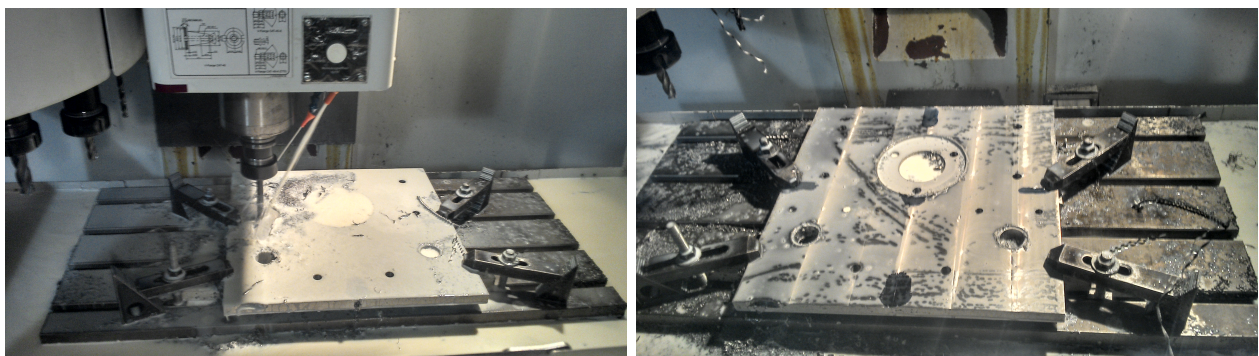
Proceso de maquinado CNC (izquierda) y pieza resultante (derecha).
